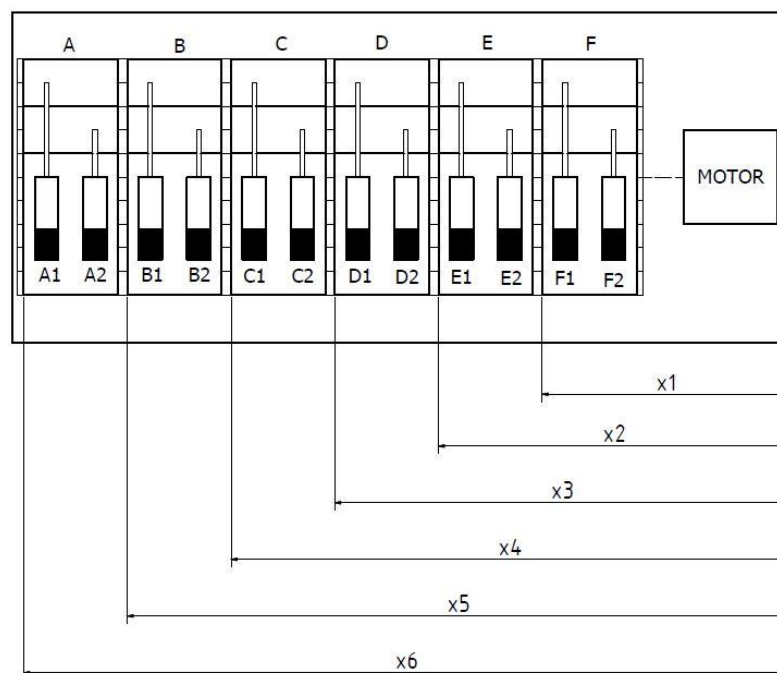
Tandemový držák kartáčů typu RD (převzato z [23].)
